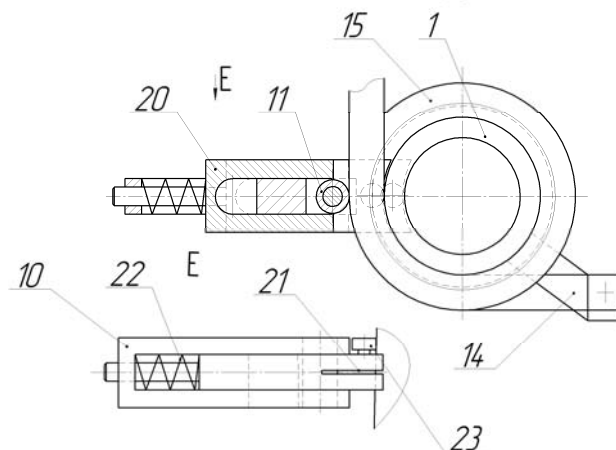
Конструкція ролика із напрямною для навивання конічних стрічкових гвинтових робочих органів
